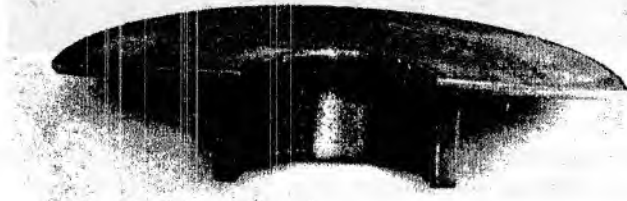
Деталь, яка виготовлена відбортовкою розкочуванням
